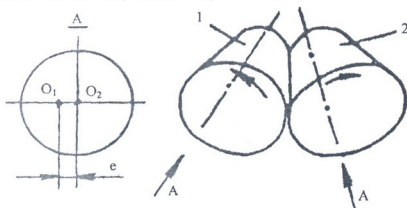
Коническая зубчатая передача с эксцентричными колесами внешнего зацепления
